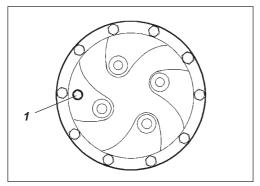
Engrenagem planetária/posição de enchimento 1. Bujão
